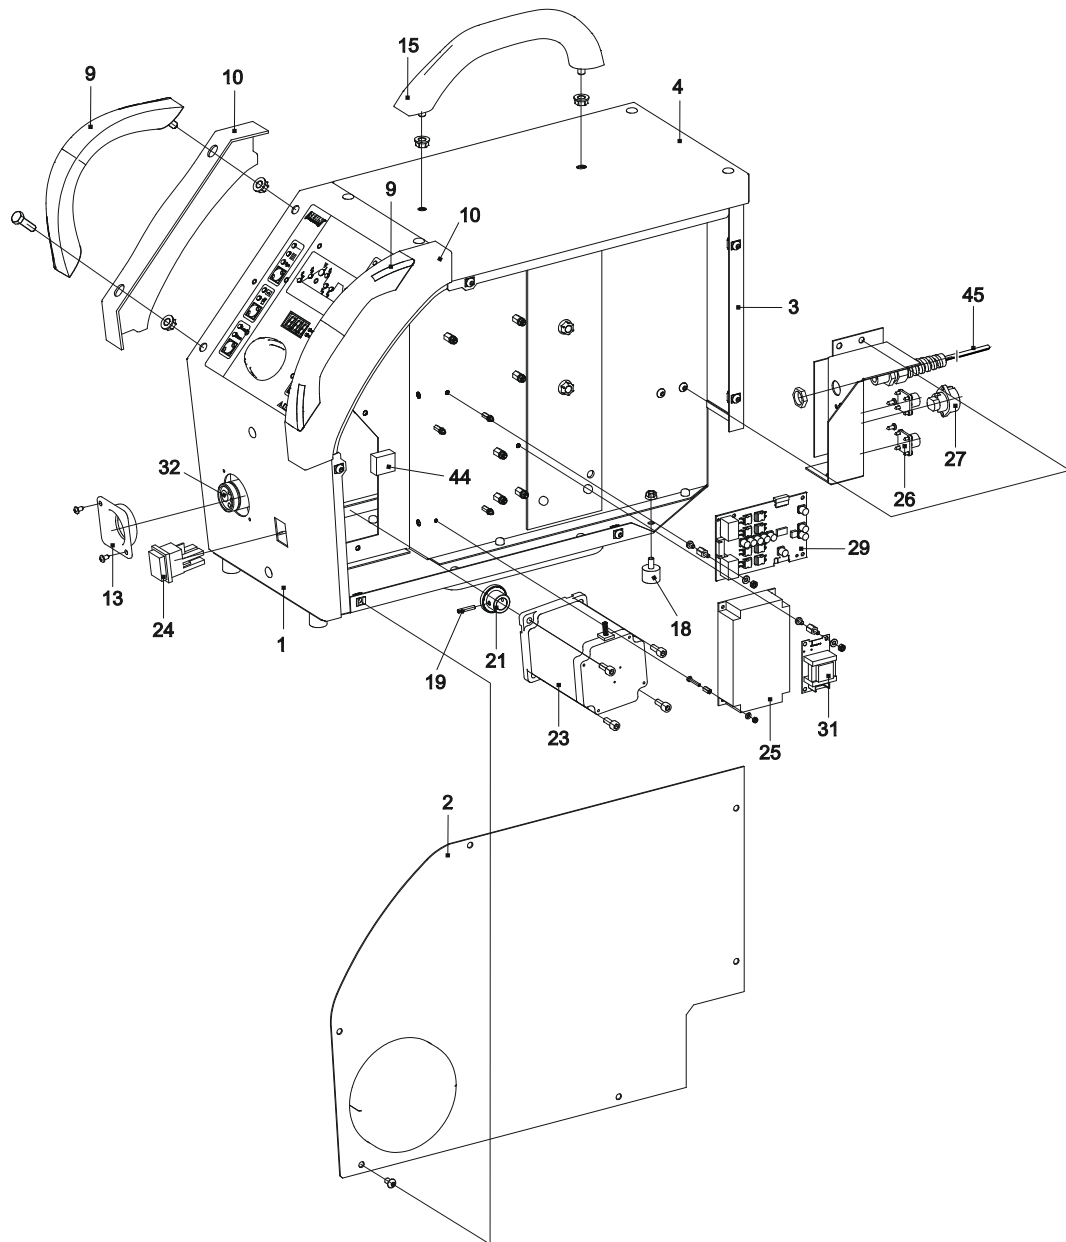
Explosionszeichnung Kaltdrahtgerät APUS 20C
